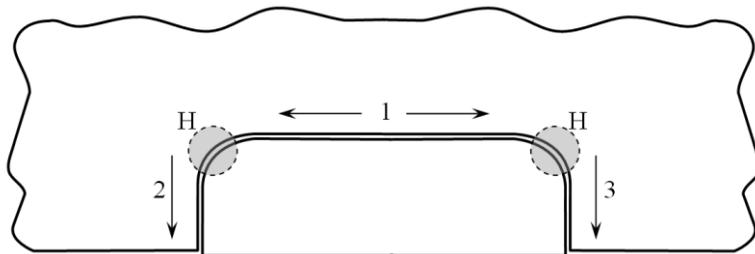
Схема установки и порядок сварки вставки, имеющей одну свободную кромку, с использованием подогрева
